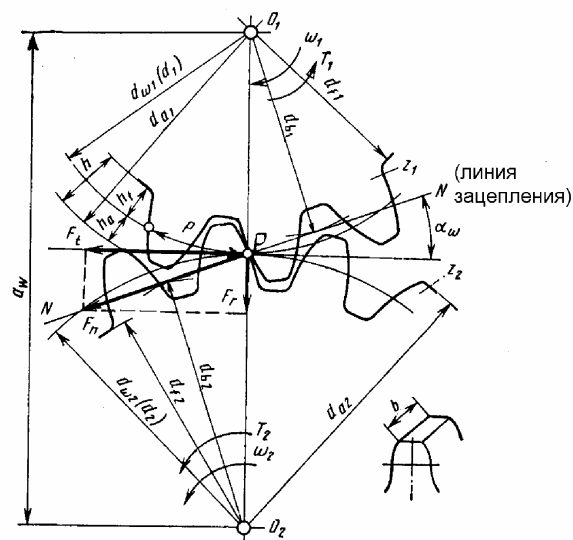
Геометрические параметры зубчатой цилиндрической передачи
